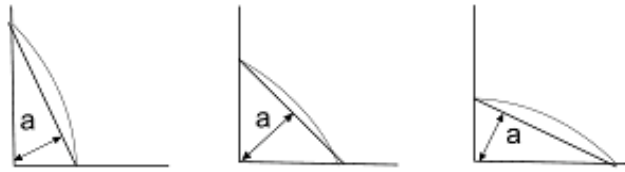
Ilustração do tamanho da garganta para diferentes configurações de cordões de soldadura.
